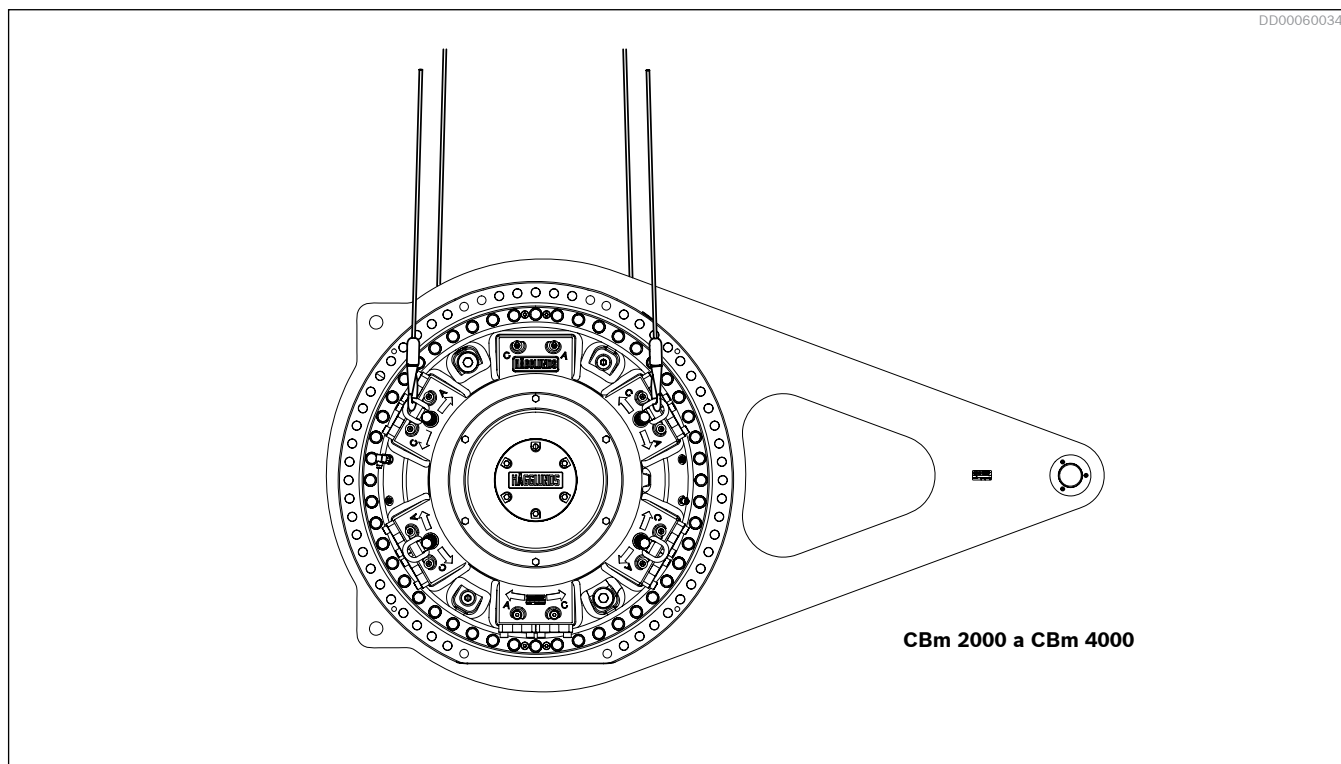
Elevação do motor e braço de torque de uma terminação montado
